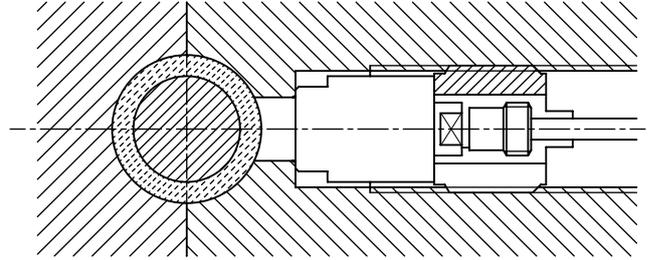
Sensor mit bearbeiteter Front nur Typ 6172BA...
